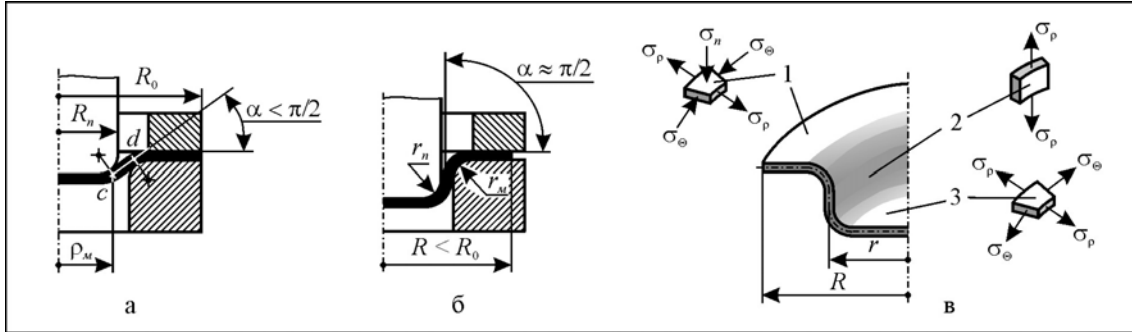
Схема витягування з притиском заготовки: а – початкова (перша) стадія; б – подальша (друга) стадія; в – напружений стан заготовки в момент другої стадії витягування; 1 – ділянка кільцевого фланцю; 2 – циліндрична ділянка; 3 – донна ділянка
